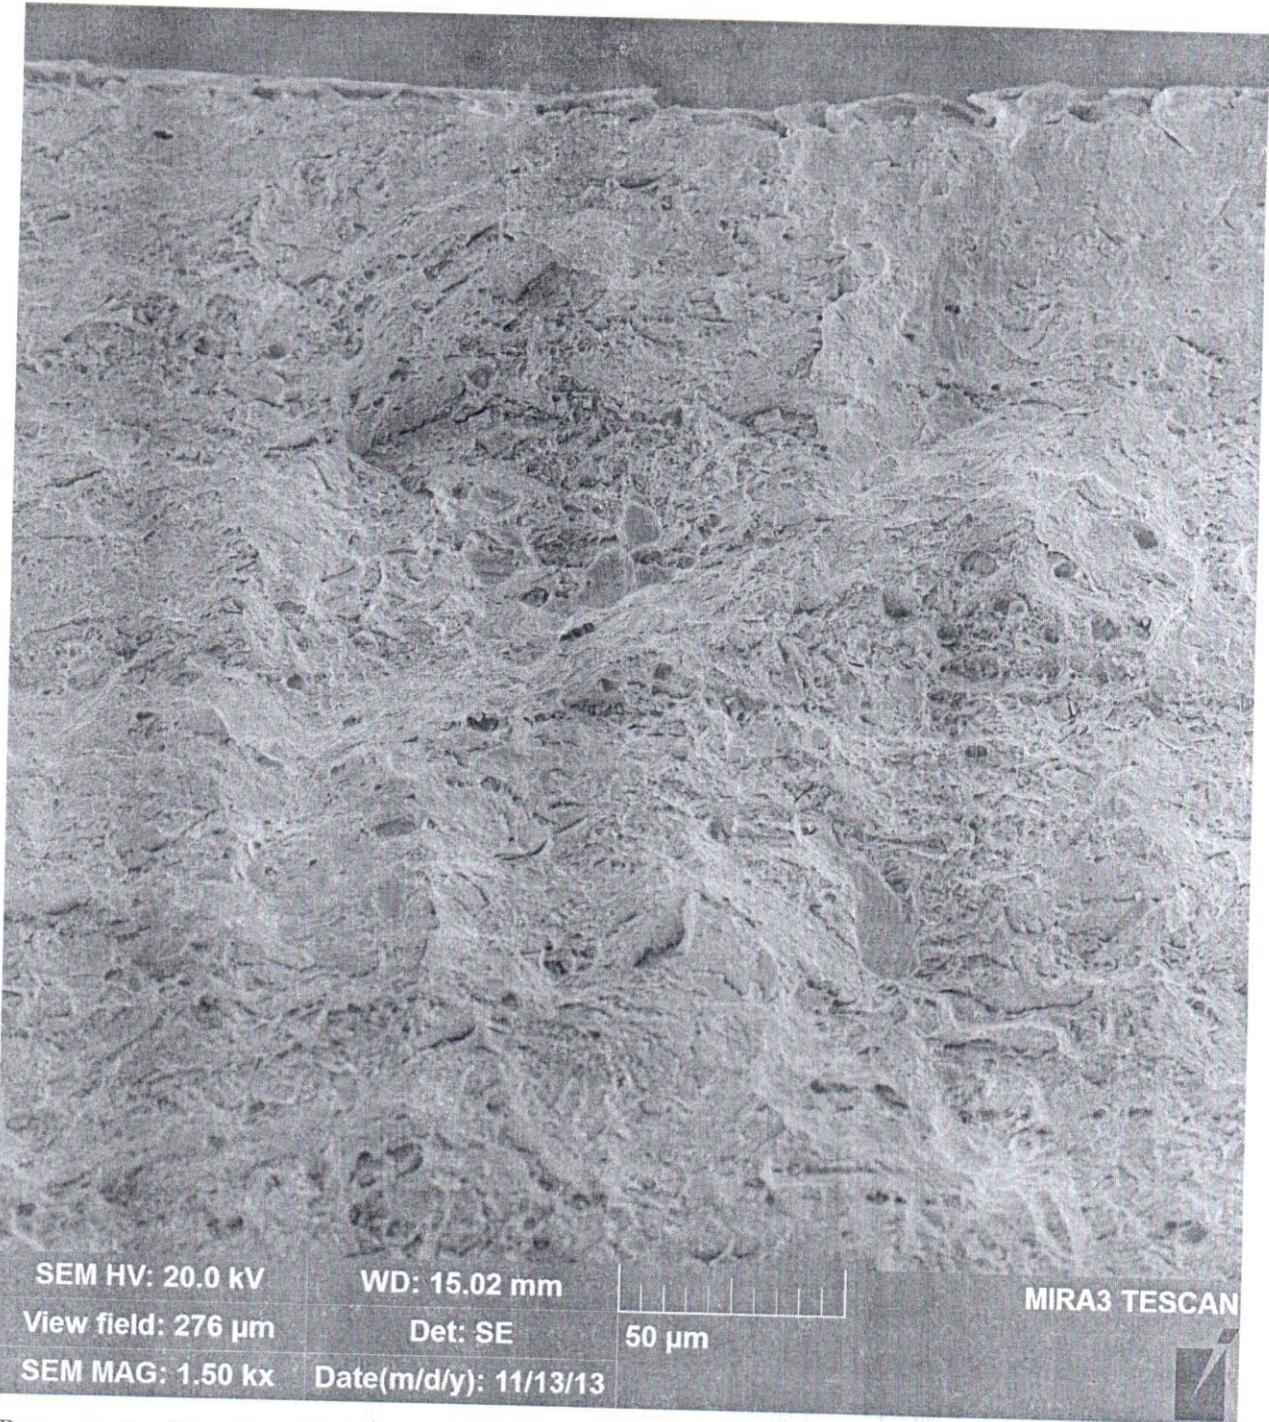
Вид поверхности разрушения образца из аустенитной стали распуханием 6%,
